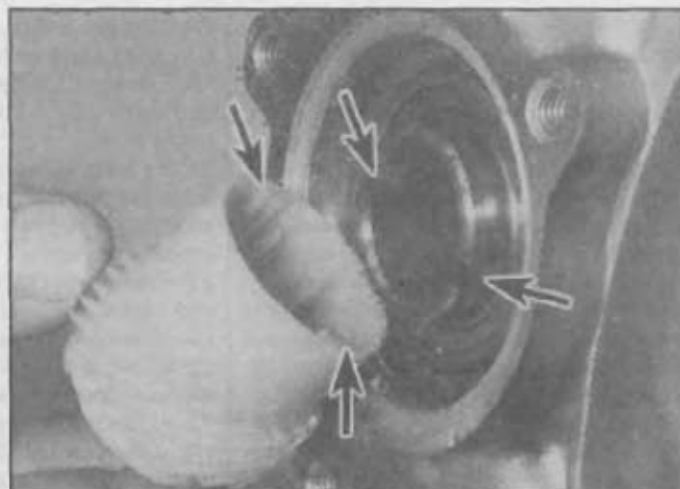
Совмещение пазов с выступами на шестерне при установке ведущей шестерни датчика скорости автомобиля
